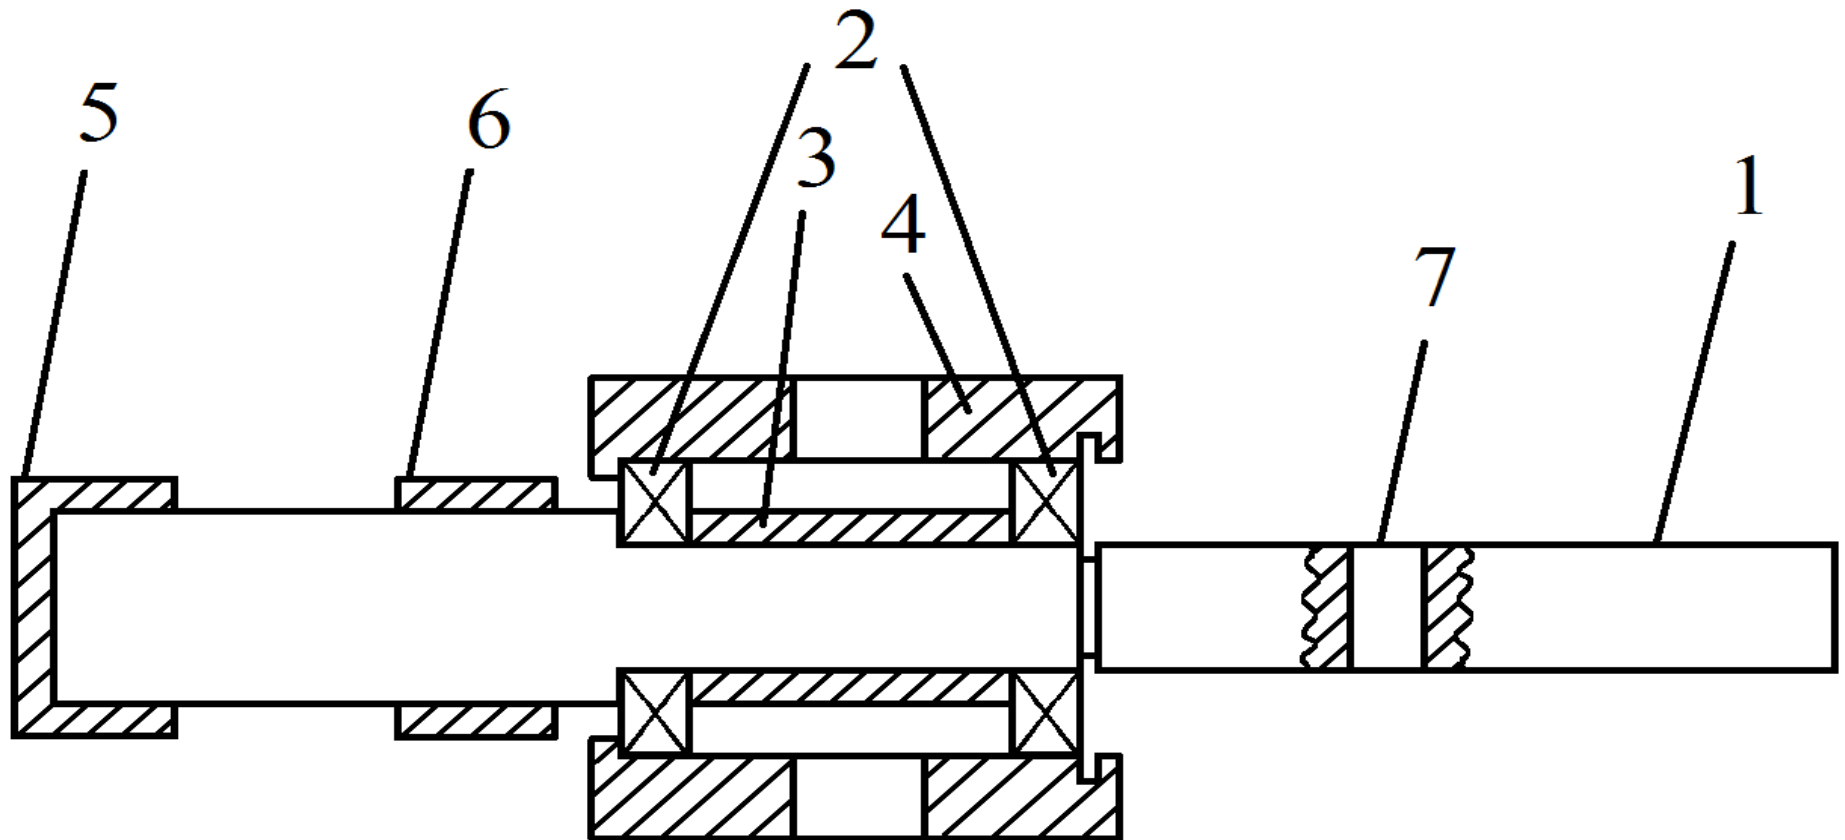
Схема узла №1: 1 – основной вал; 2 – подшипники качения; 3 – стопорная втулка; 4 – внешняя втулка с пазами для спиц; 5 – настенное крепление; 6 – напольное крепление; 7 – паз под побочный вал.
